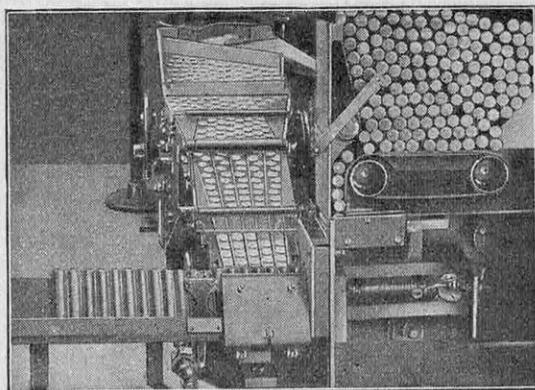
LE REMPLISSAGE AUTOMATIQUE DES TUBES PAR UNE MACHINE COMPTEUSE.
